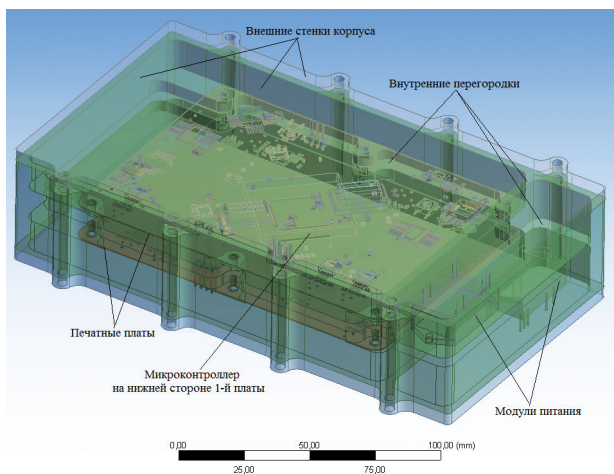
Вид проектируемого корпуса РЭА с прозрачными стенками
